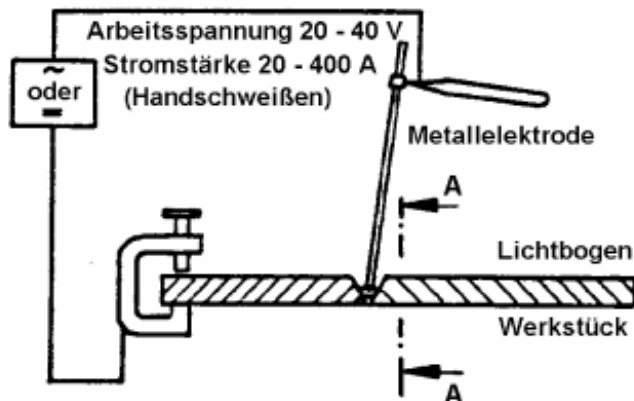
Prinzip der Handschweißung mit Stabelektrode
